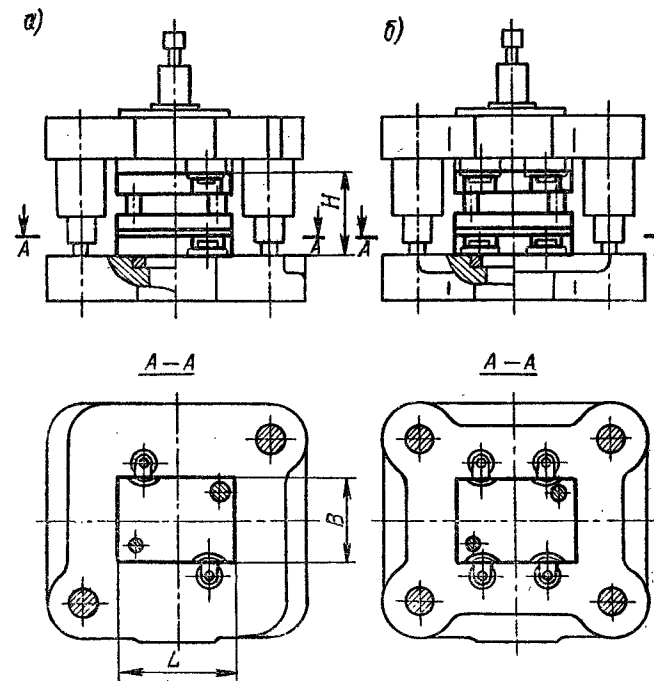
Универсальный блок для крепления сменных пакетных штампов
